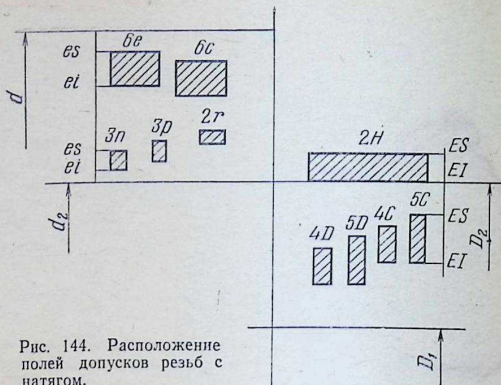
Расположение полей допусков резьб с натягом.
